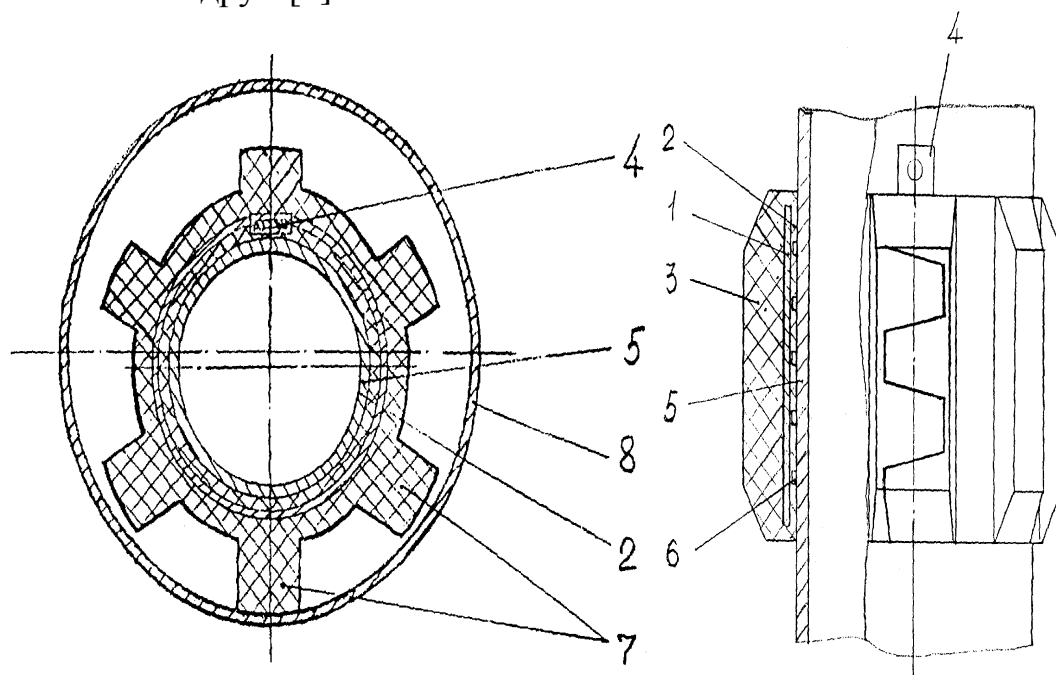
Устройство для предохранения от взаимного истирания труб: 1- металлический корпус, 2 – внутренний эластичный элемент, 3 – наружный эластичный элемент, 4 – механизм запирания, 5 – бурильная труба, 6 – кольцевые канавки, 7 – ребра, 8 – стенка обсадной трубы.
